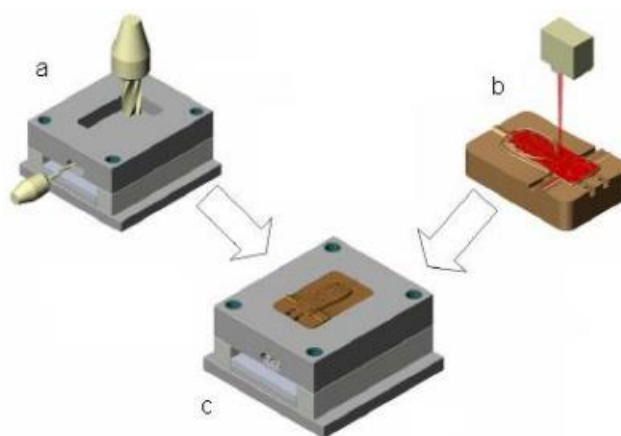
Conceito de Molde Híbrido: (a) estrutura do molde fabricado convencionalmente; (b) inserto fabricado por adição de camadas e (c) molde com o inserto montado.
